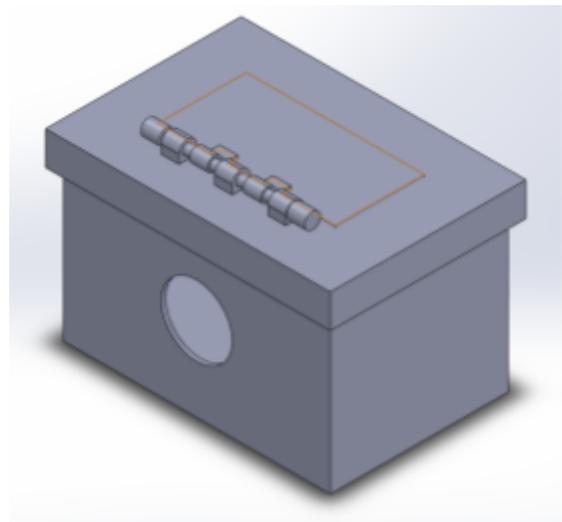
vue isométrique de derrière de la boîte de composants électroniques en modèle 3D
